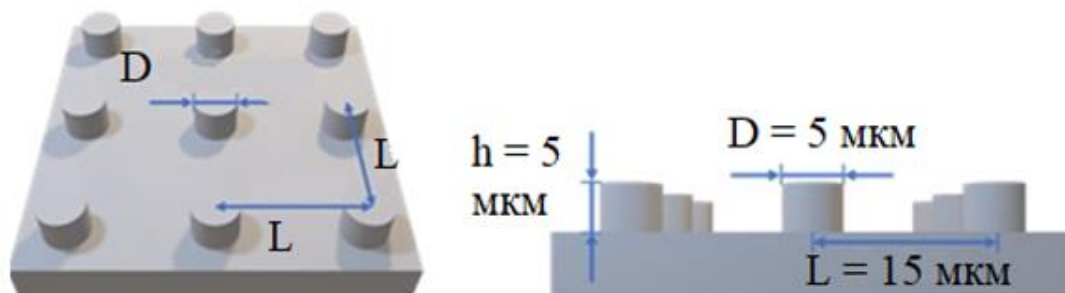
Внешний вид и размеры изделия ТЗ№2.
